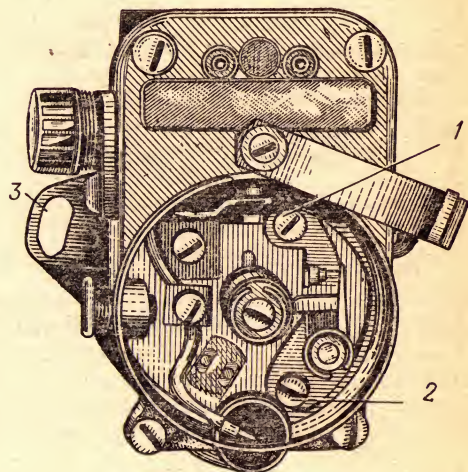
Регулировка зазора между контактами прерывателя магнето:
